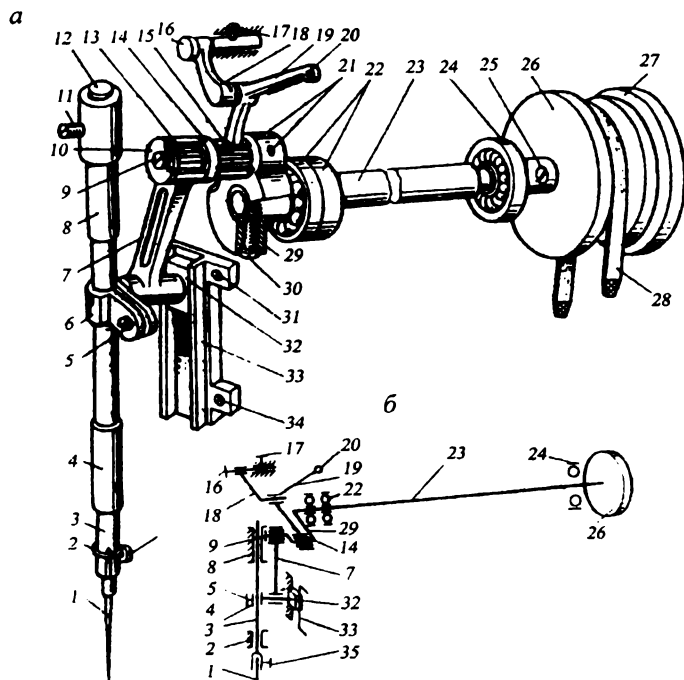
Конструкция механизма движения иглы машины 1022-М кл. ОЗЛМ:
